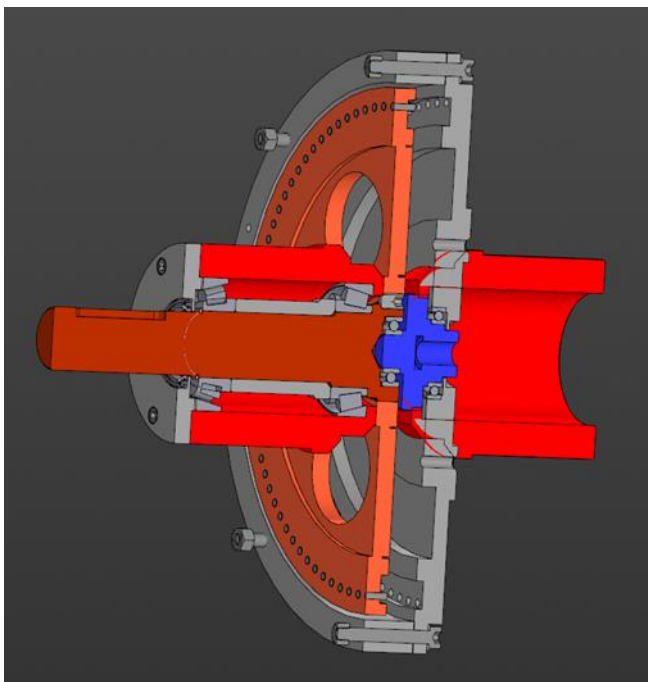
Редуктор орбитальный без зубчатый редуктор (3D модель)
